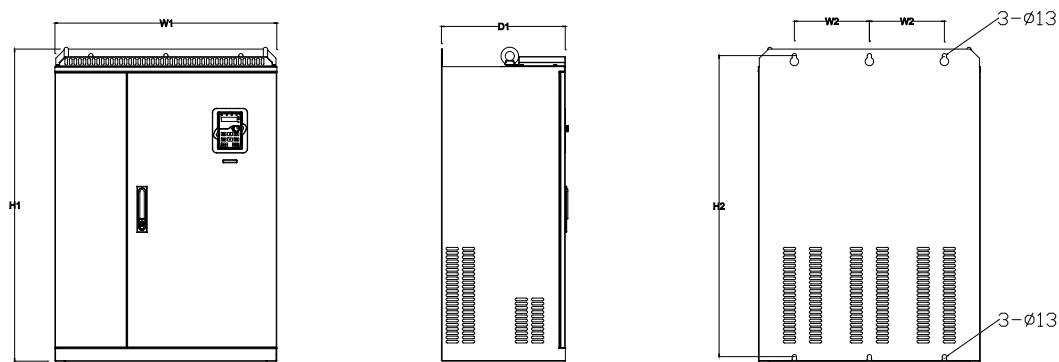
Настенный монтаж 220 – 315 кВт
